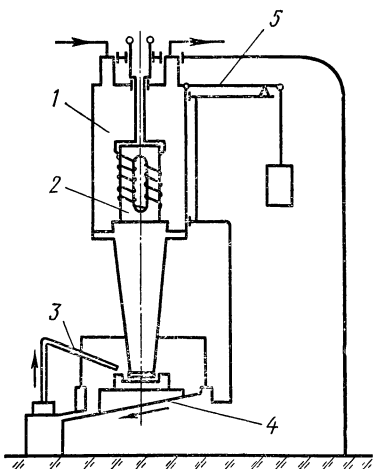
Принципиальная схема ультразвукового станка для обработки твердых хрупких материалов:
